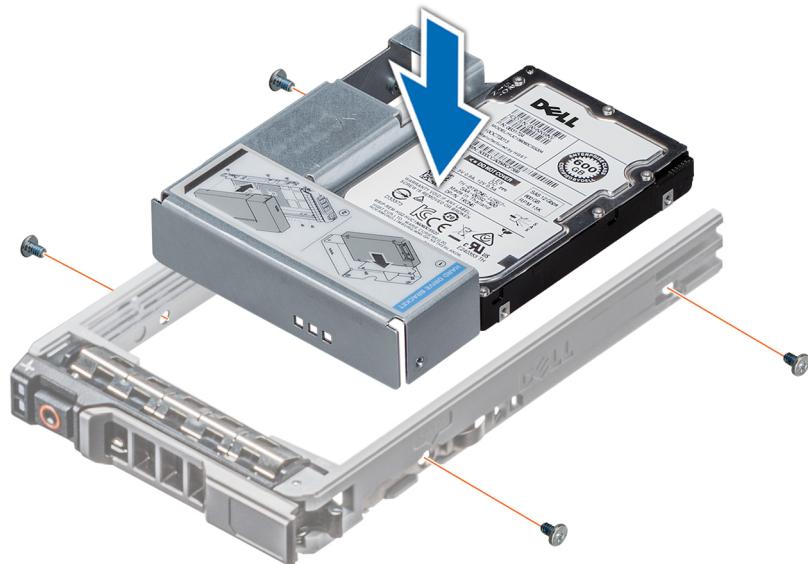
Installation d'un adaptateur de disque 3,5 pouces dans un support de disque 3,5 pouces
